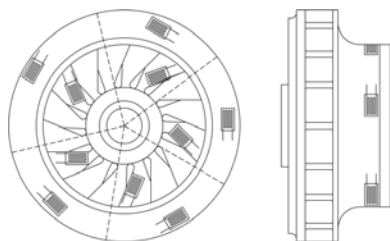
Схема разрезки рабочего колеса турбины и установки тензорезисторов
